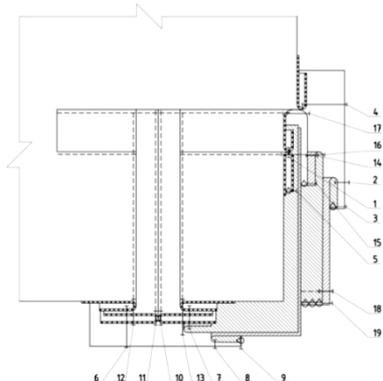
Сборочный чертеж прорезного кармана с двумя накладывающимися линиями входа
